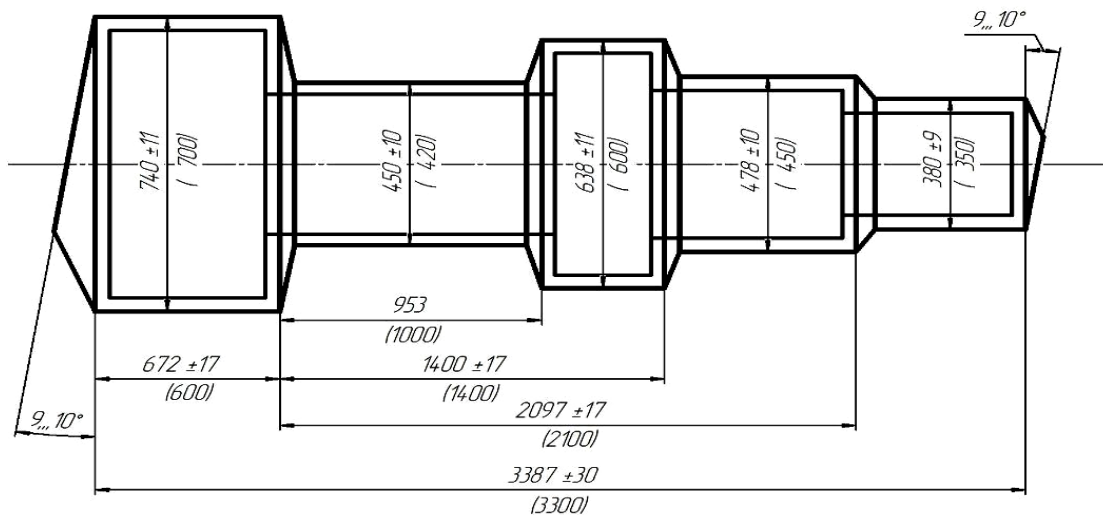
Приклад креслення поковки, яку виготовляють куванням на пресі
